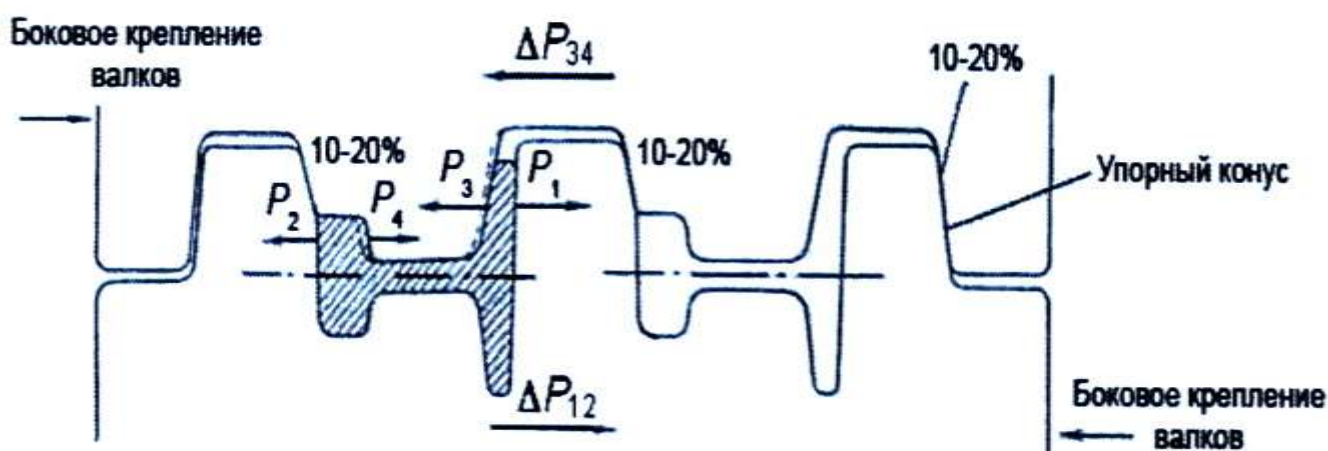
Расположение рельсового калибра на валках и схема возникновения осевых сил [165]
